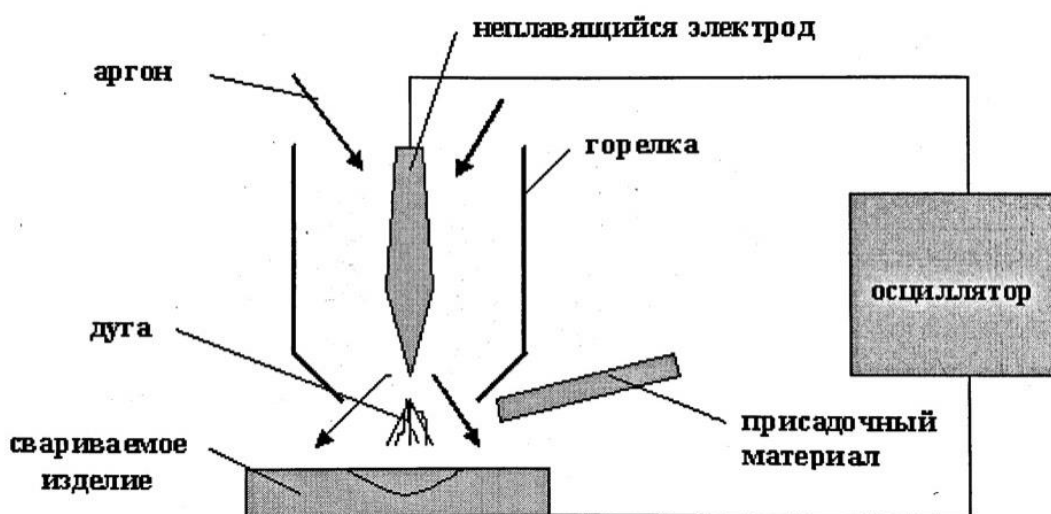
Принцип работы аргонодуговой сварки неплавящимся электродом [6]
